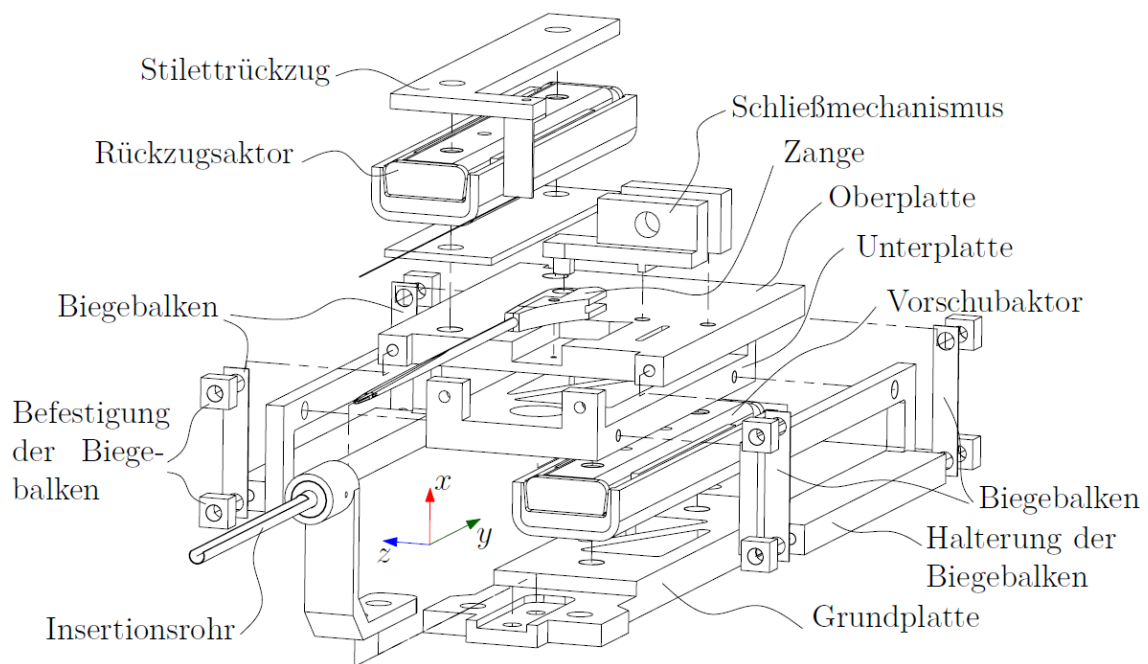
Explosionszeichnung des am imes entwickelten, kraftsensorischen Insertionstools.
